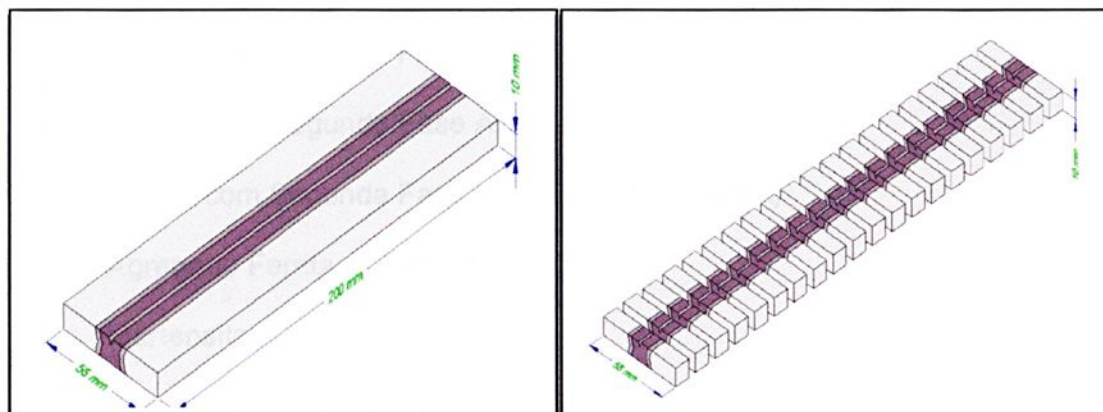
Corpo de prova soldado, usinado e cortado.
